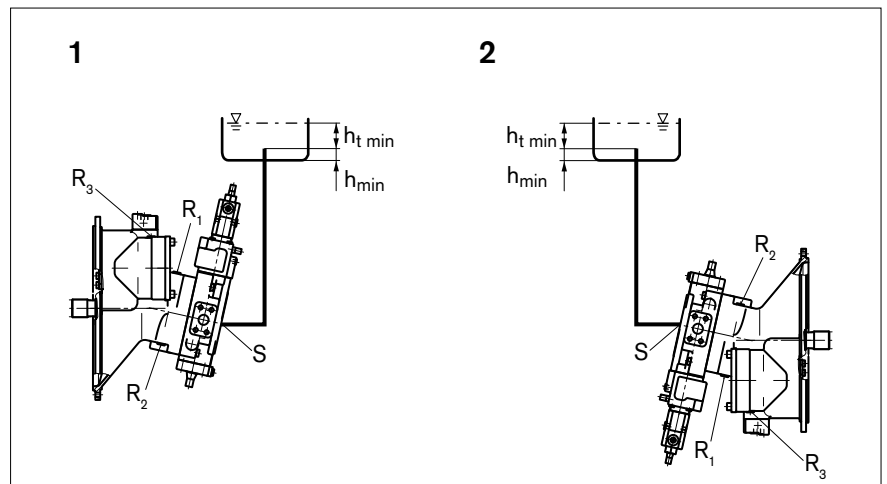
Untertankeinbau mit Einbaulage 1–2
